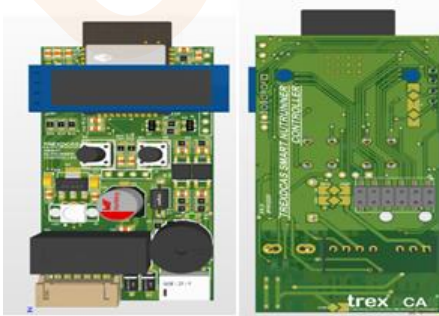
Elektronik Kartın Üst Kat PCB Tasarımı
